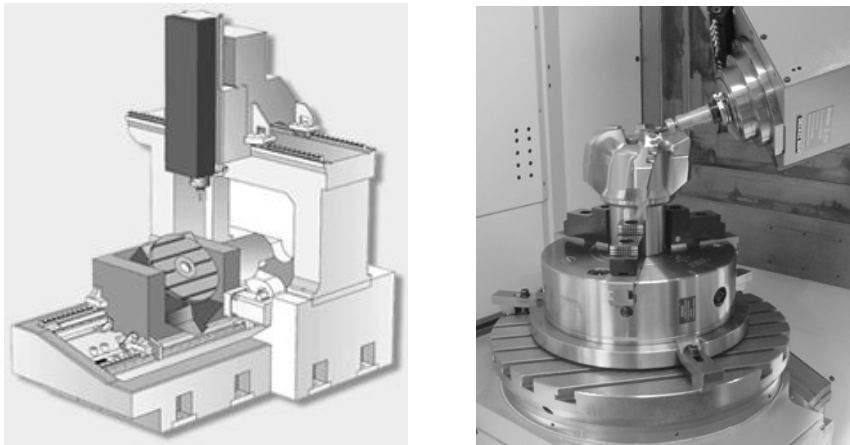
Exemple de machines de type RRTTT et de type RTTTR
